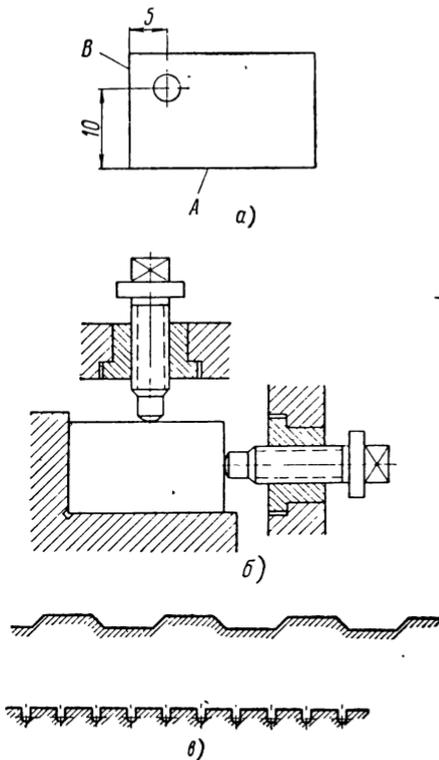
Схема установки детали: а — по установочным плоскостям, б — по установочному элементу приспособления, в — по прерывистой установочной поверхности
